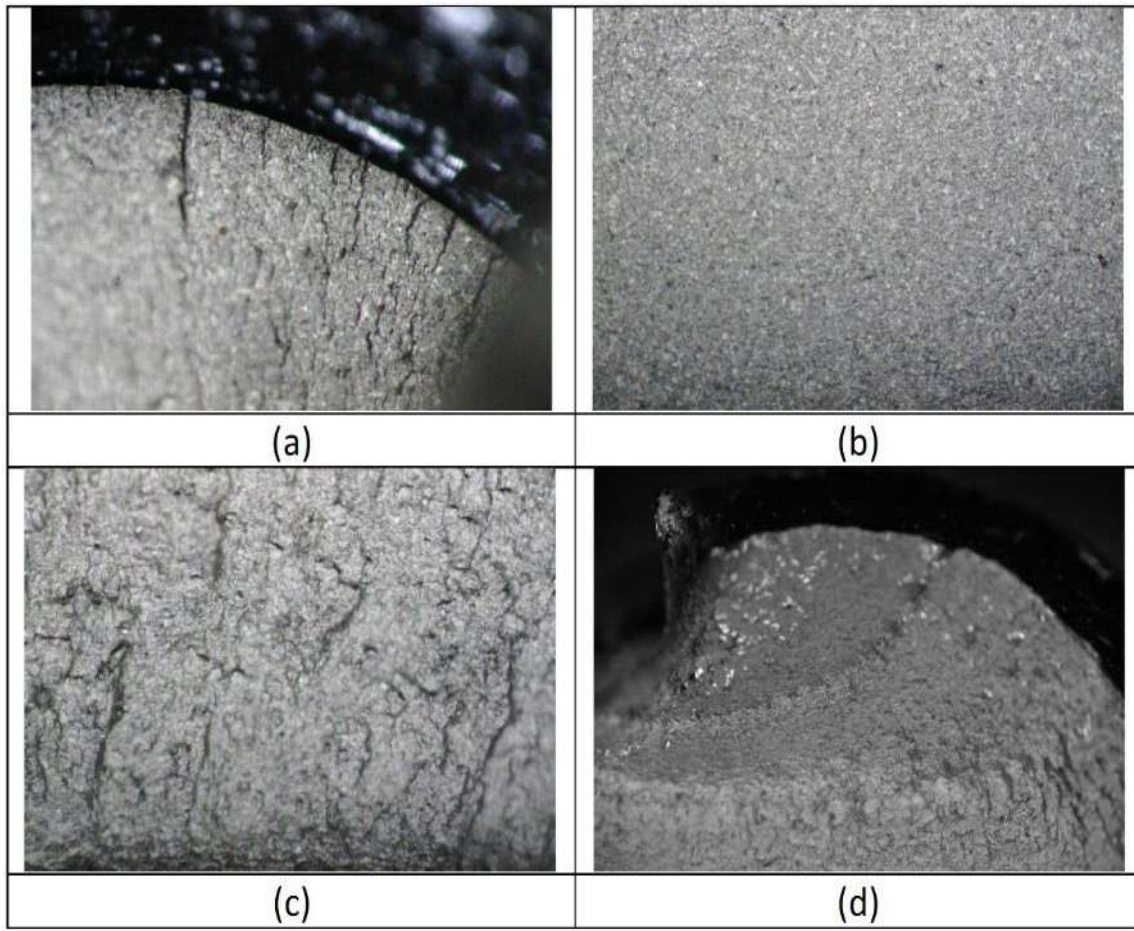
Superficie de fractura de los tornillos. (a) Múltiples sitios de iniciación y marcas de trinquete debido a la convergencia de la superficie de la grieta. (b) Superficie relativamente lisa de crecimiento estable de grietas. (c) Superficie de fractura rugosa. (d) Labio de corte.
